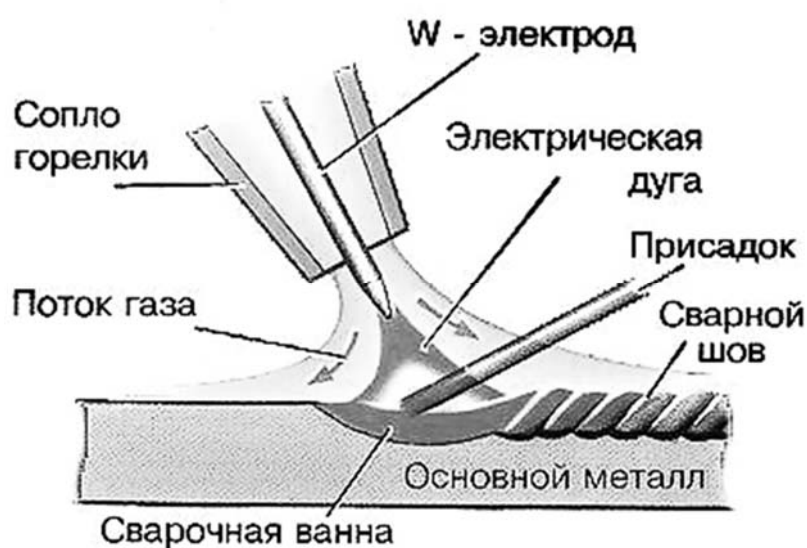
Схема сварки неплавящимся вольфрамовым электродом в защитном газе
